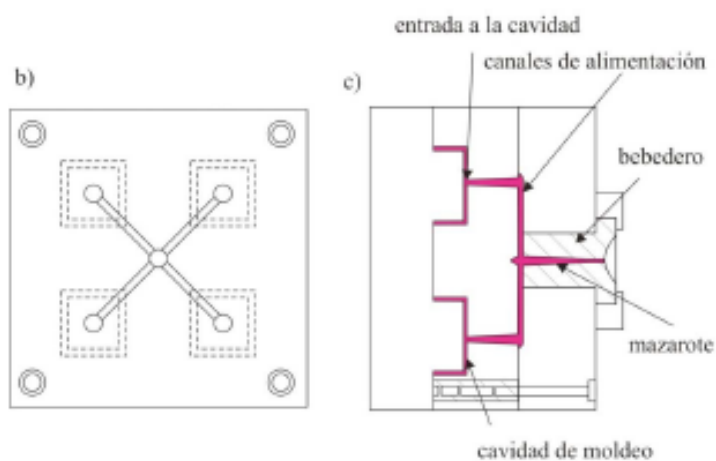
Parts principals d'un motlle senzill (2)
